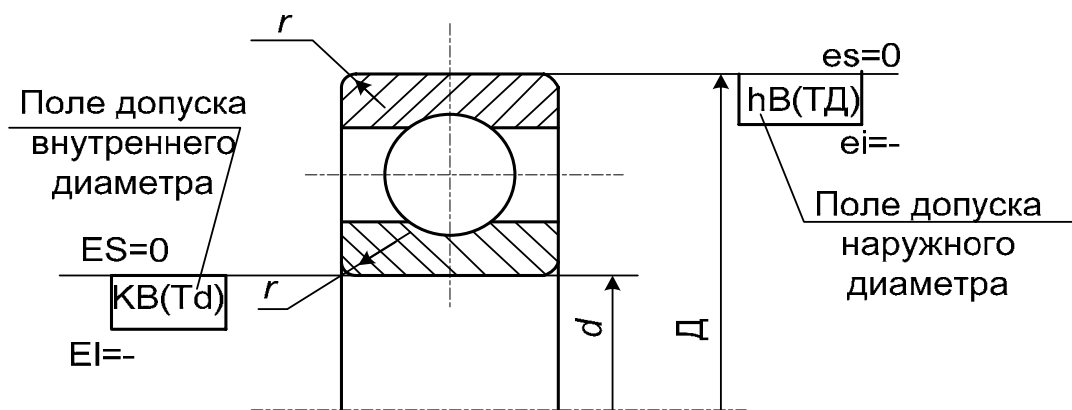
Схемы расположения полей допусков на диаметры колец подшипников качения требуемых рабочих зазоров
